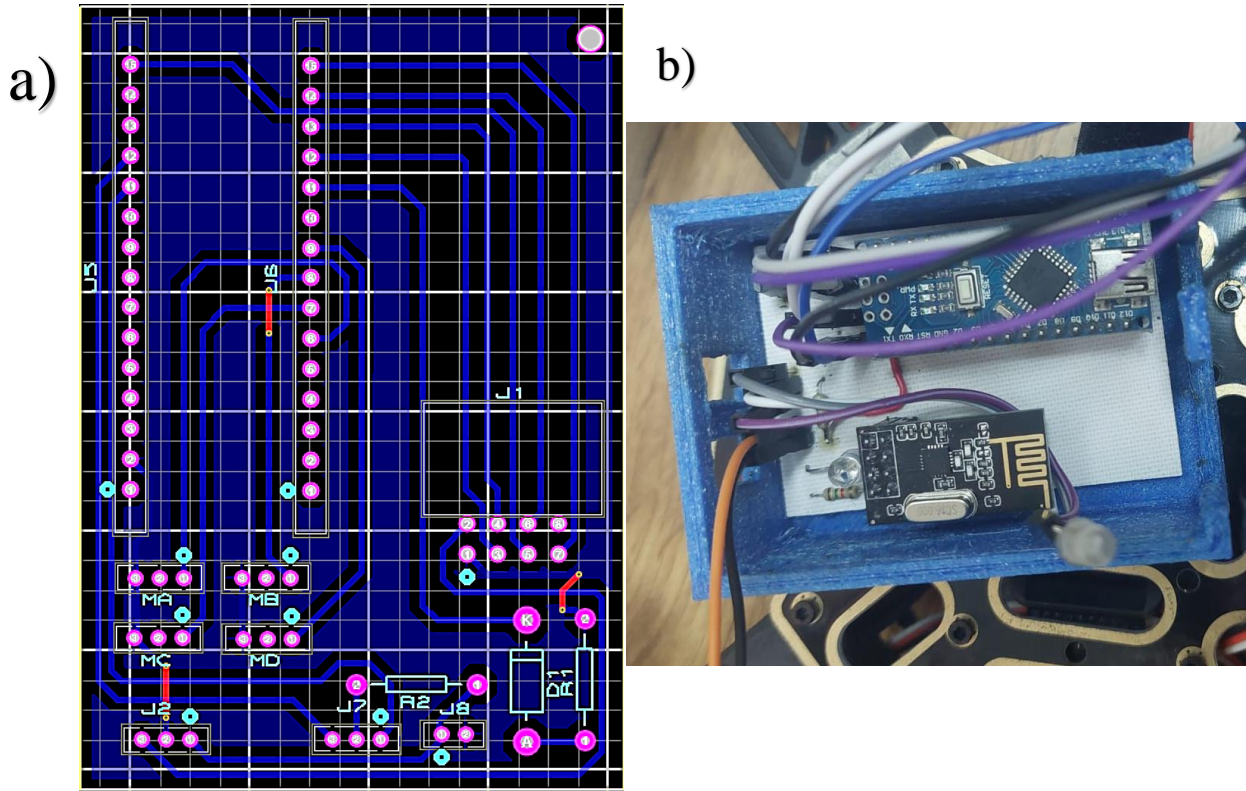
a) PCB del cuadricóptero, b) PCB física del cuadricóptero.
